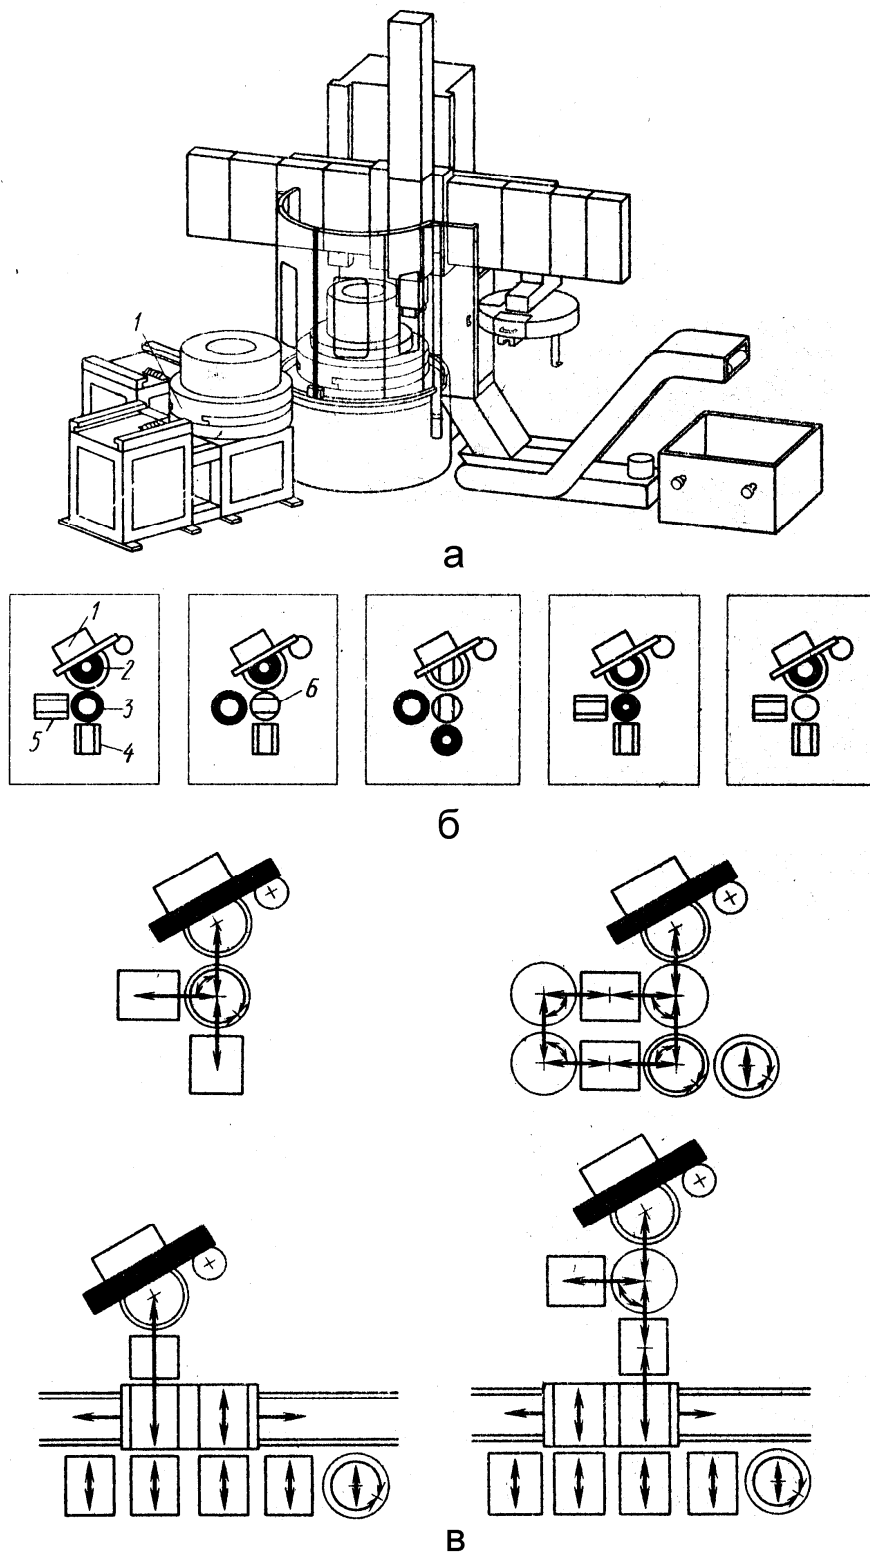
ГВМ фірми «Шісс Фроріп»: а – загальний вигляд ГВМ з тримісним приймально-передавальним пристроєм: 1 – приймально-передавальний механізм; б – фази маніпулювання двома деталями: 1 – верстат; 2 – заготовка; 3 – оброблена деталь ; 4, 5 – друга і третя позиції приймально-передавального механізму; 6 – поворотна позиція приймально-передавального механізму; в – варіанти нарощування місткості приймально-передавального механізму
